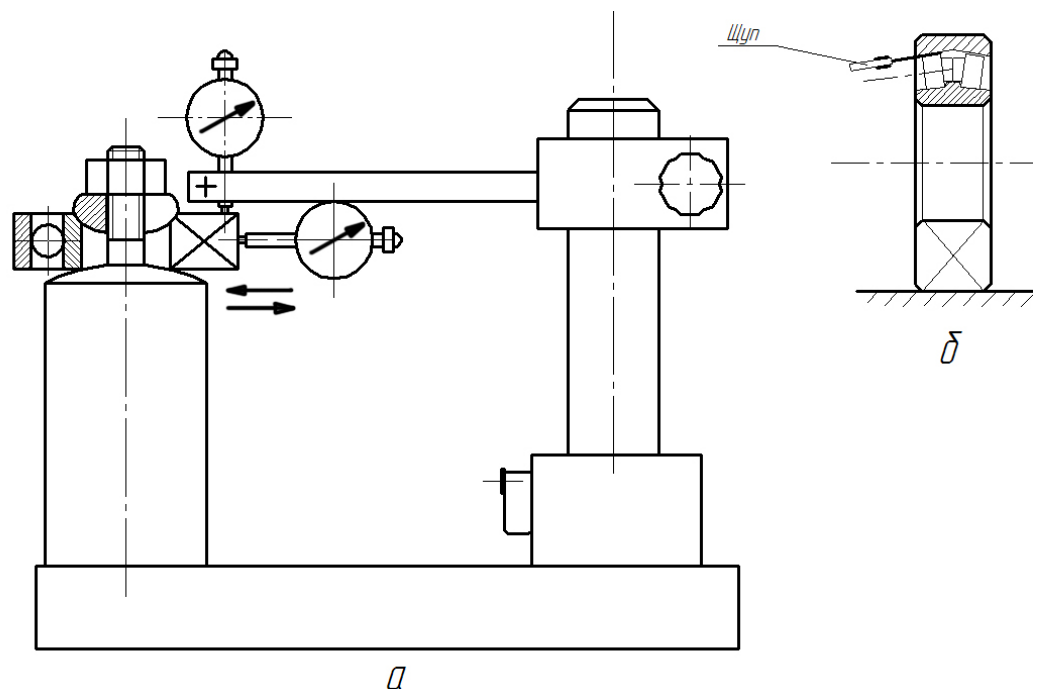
Схема определения величины зазора в подшипниках а) шариковых; б) роликовых.
